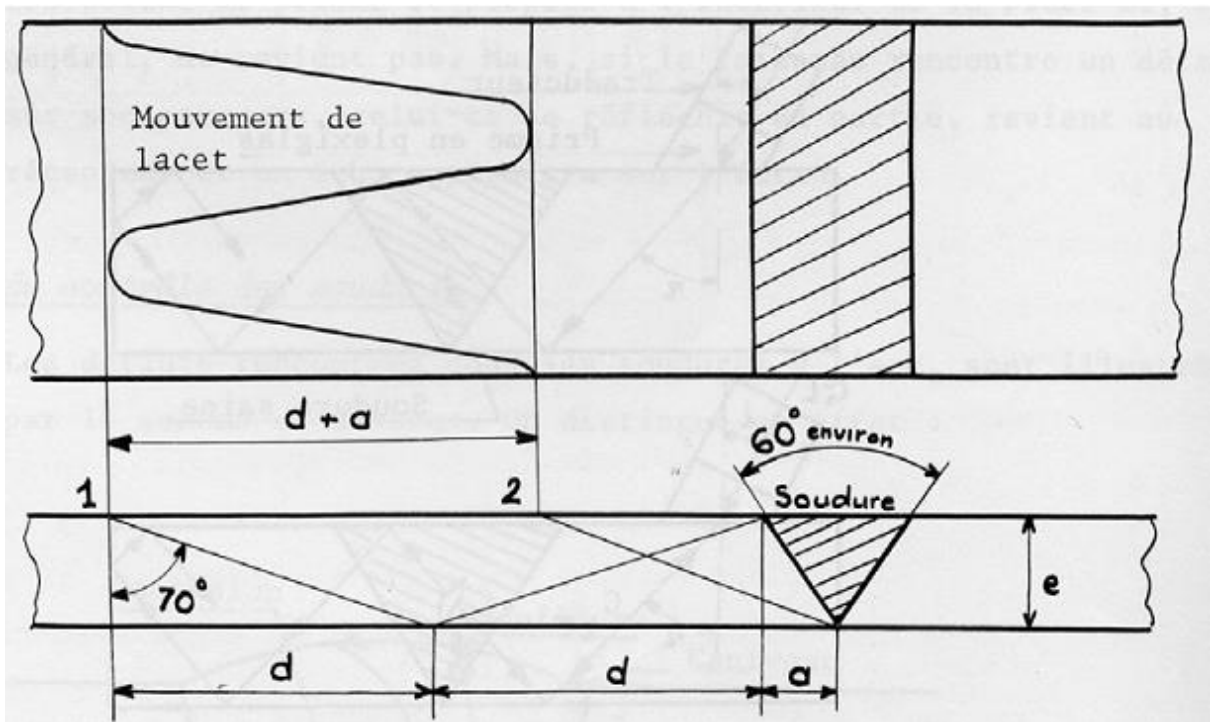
Zone d'exploration d'une soudure [18].
